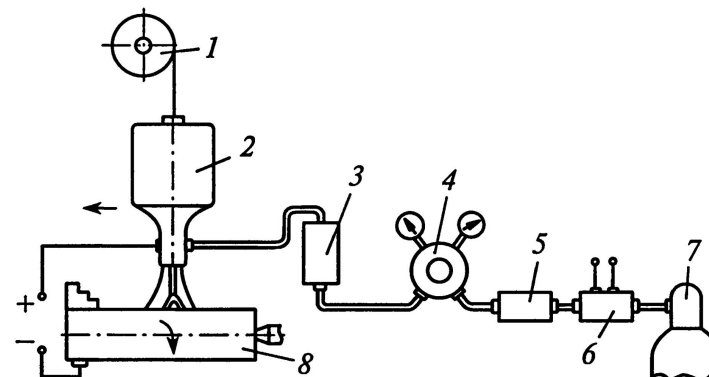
Схема установки для дуговой наплавки в углекислом газе:
